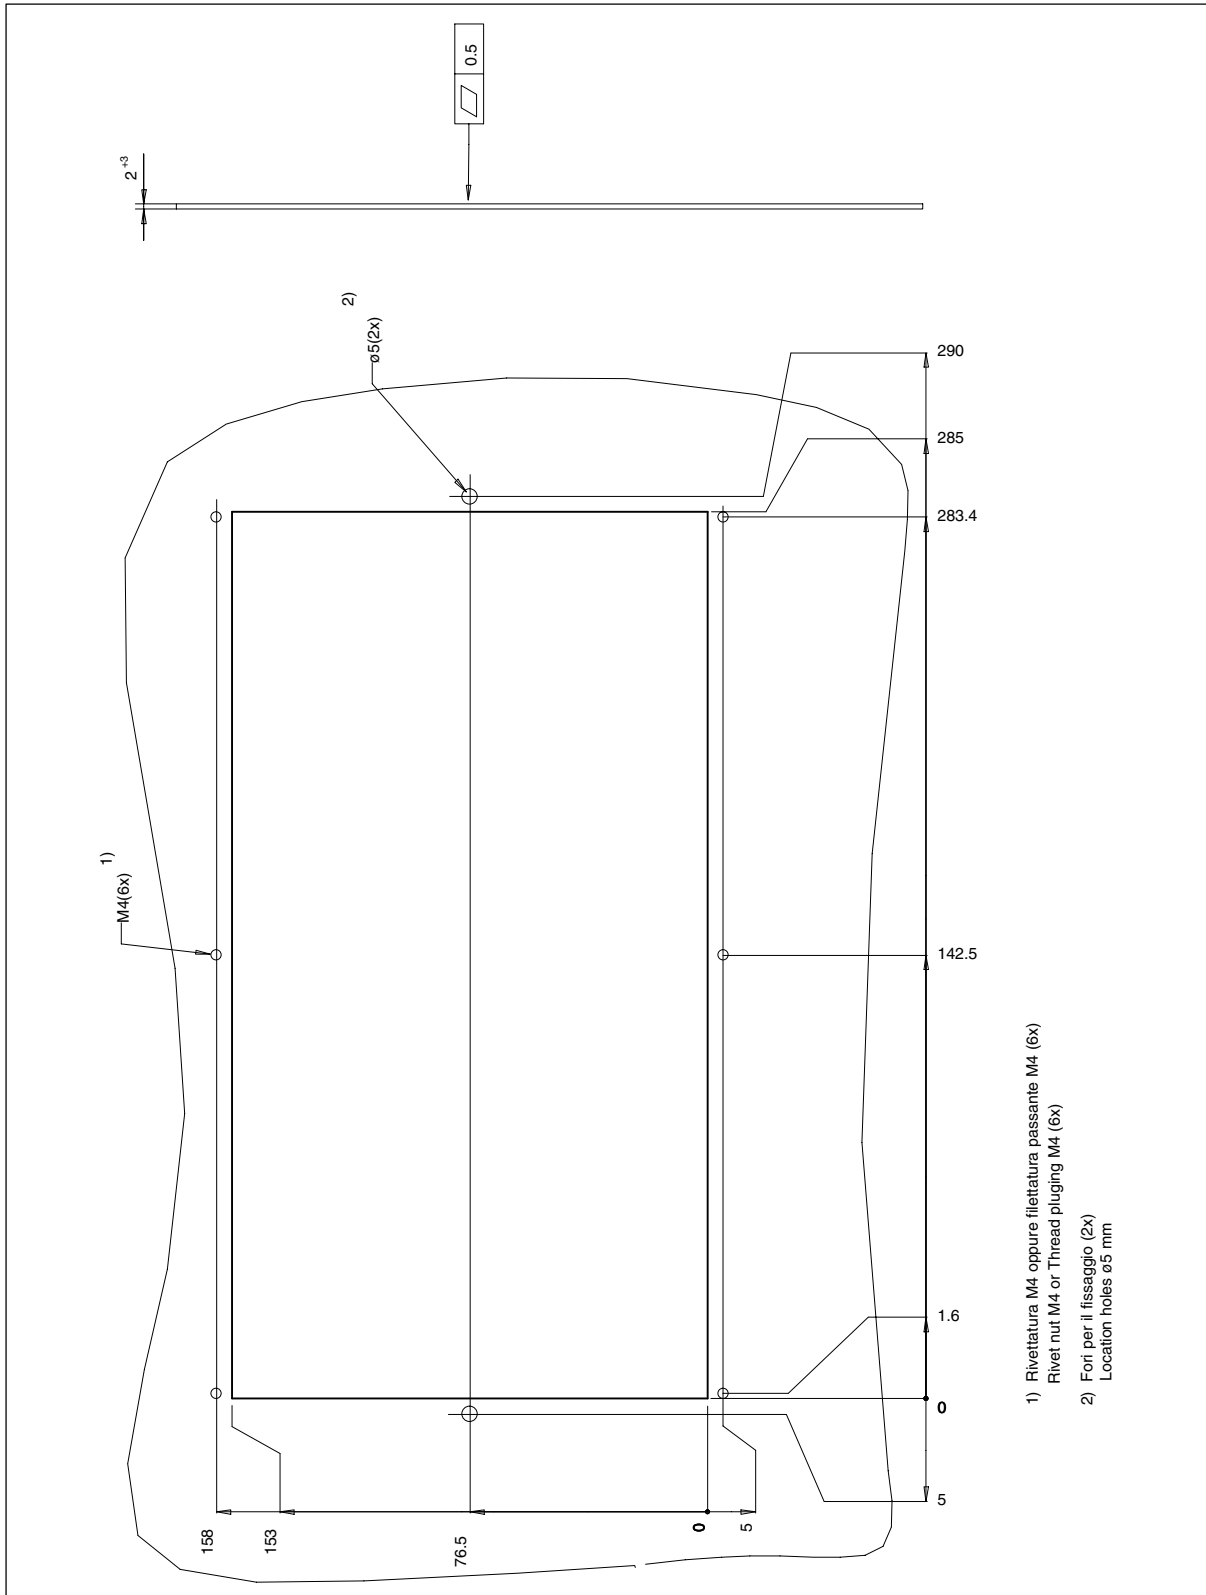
Dima di foratura Keyboard (layout orizzontale per il montaggio sotto alla PCU)
